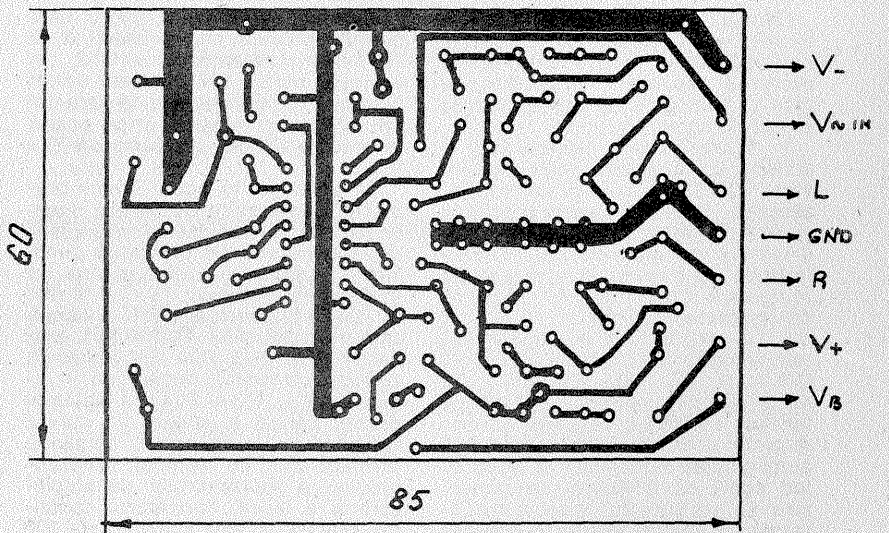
Placa de cablaj imprimat (văzută dinspre cablaj)
